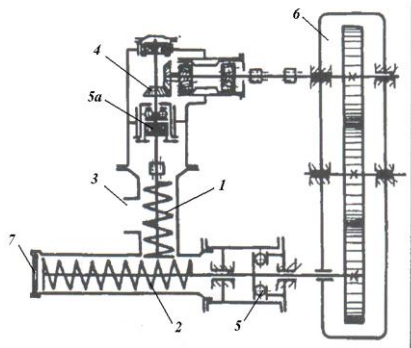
Схема шнек-преса Ш-2В: 1 – живильний шнек; 2 – пресовий шнек; 3 – завантажувальна горловина; 4 – кінцева передача; 5, 5 а – напoлегливі підшипники; 6 – редуктор; 7 – матрична обойма
